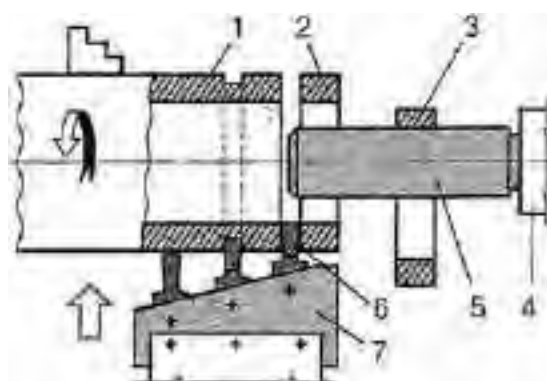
СХЕМА ВІДРІЗАННЯ КІЛЕЦЬ З ТРУБЧАТОЇ ЗАГОТОВКИ:
